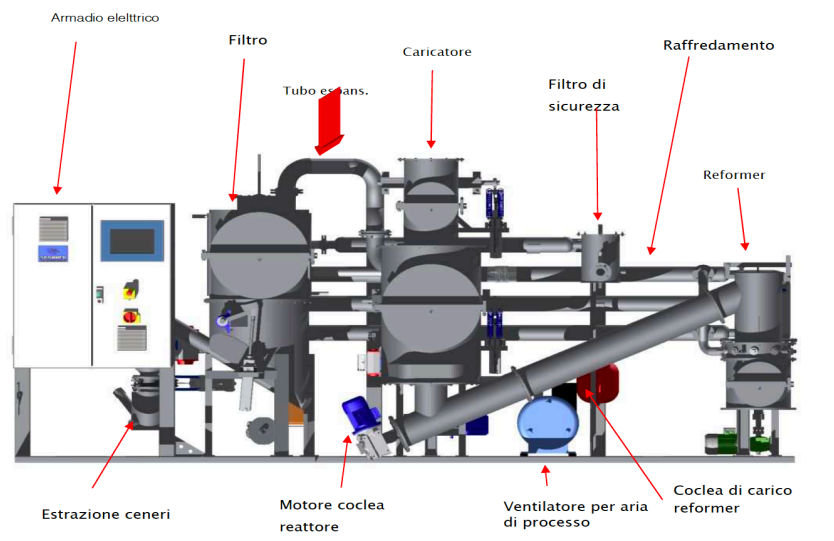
Rappresentazione schematica dell'impianto pilota SPANNER.
